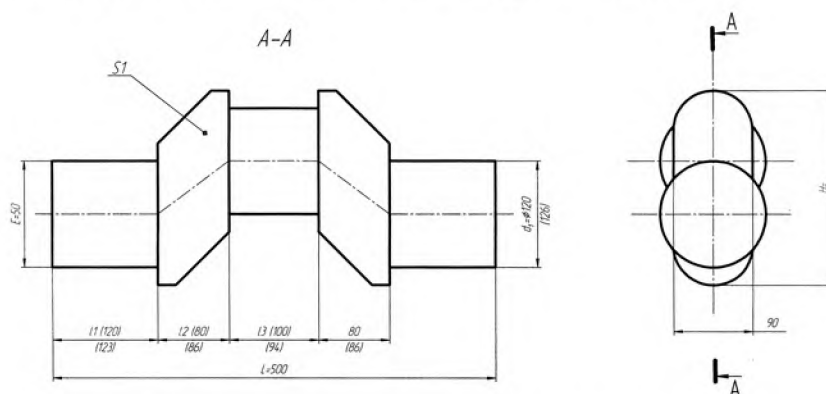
Эскиз детали «коленвал» из стали 40Х2Н3МВТ
